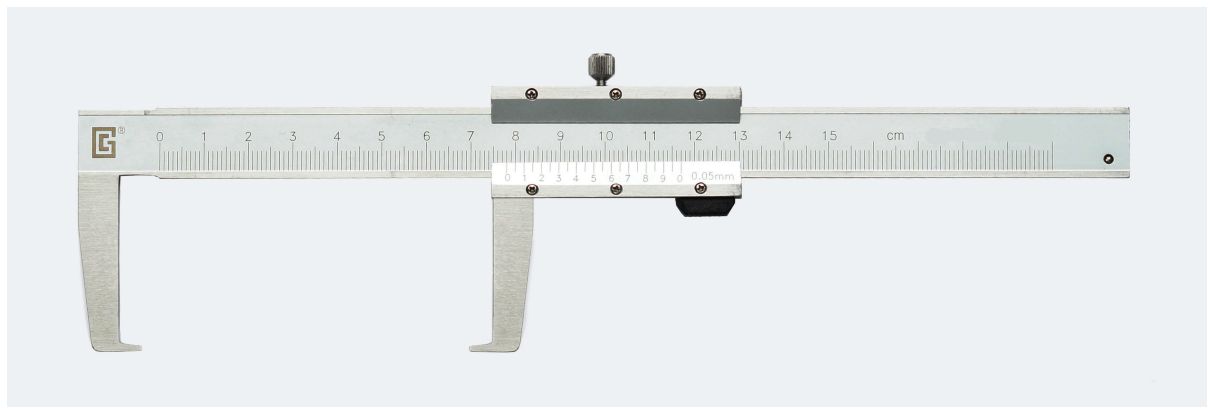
Общий вид штангенциркулей модели ШЦС-116, тип А
